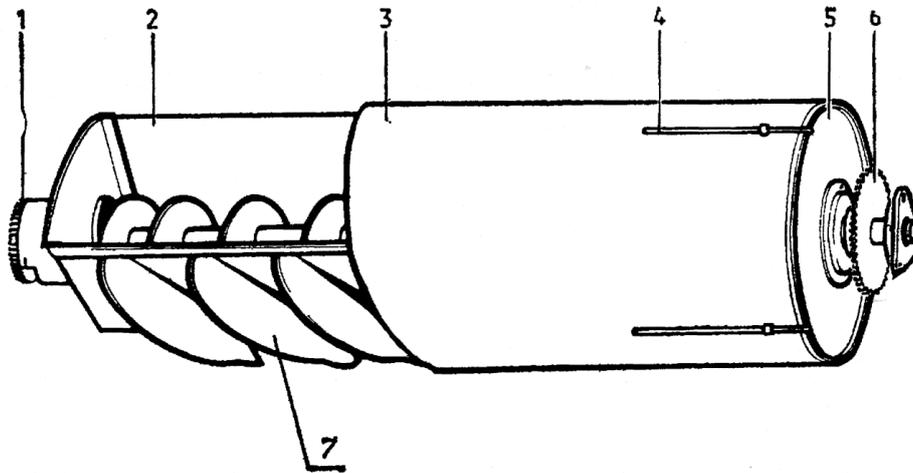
Триерный цилиндр: 1 - зубчатое колесо; 2 - лоток; 3 - обечайка; 4 - стяжка; 5 - розетка; 6 - приводная звездочка; 7 – плужок
